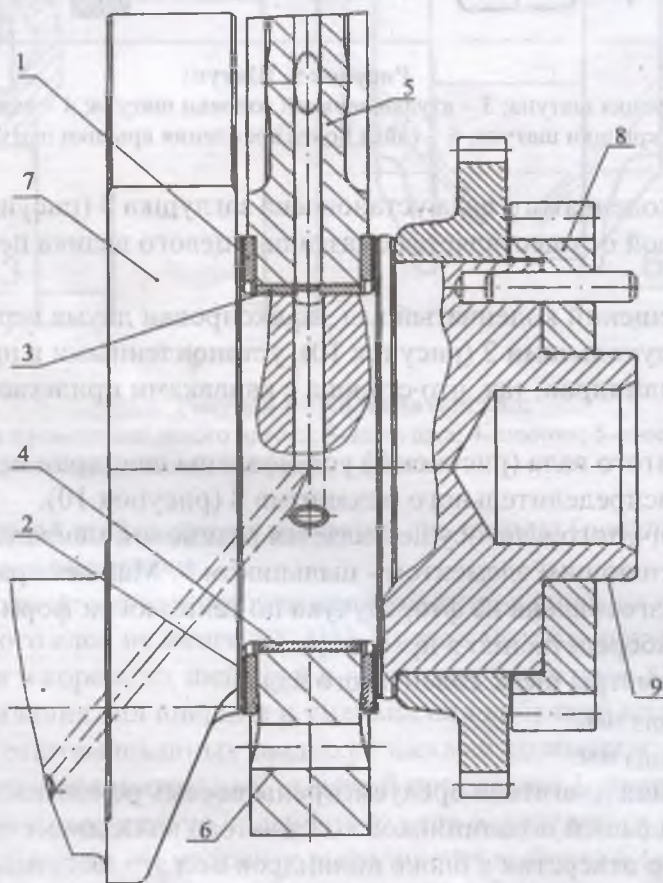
Установка упорных полуколец и вкладышей коленчатого вала:
